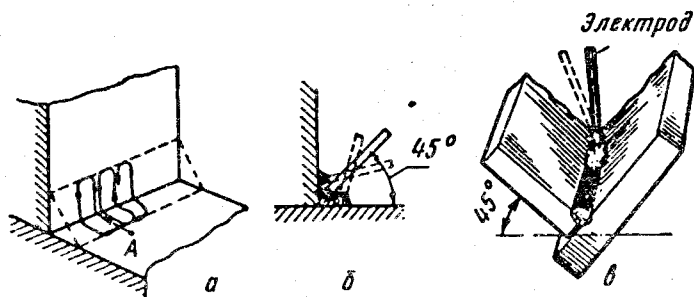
Сварка угловых швов: а — траектория движения электрода; б — изменение угла наклона электрода; в — сварка в лодочку
